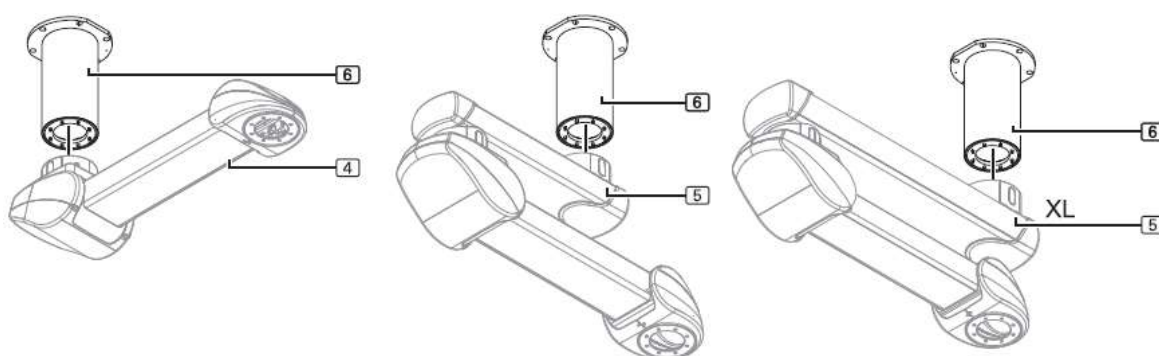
COLUMN MOTOR, COLUMN MOTOR XL
